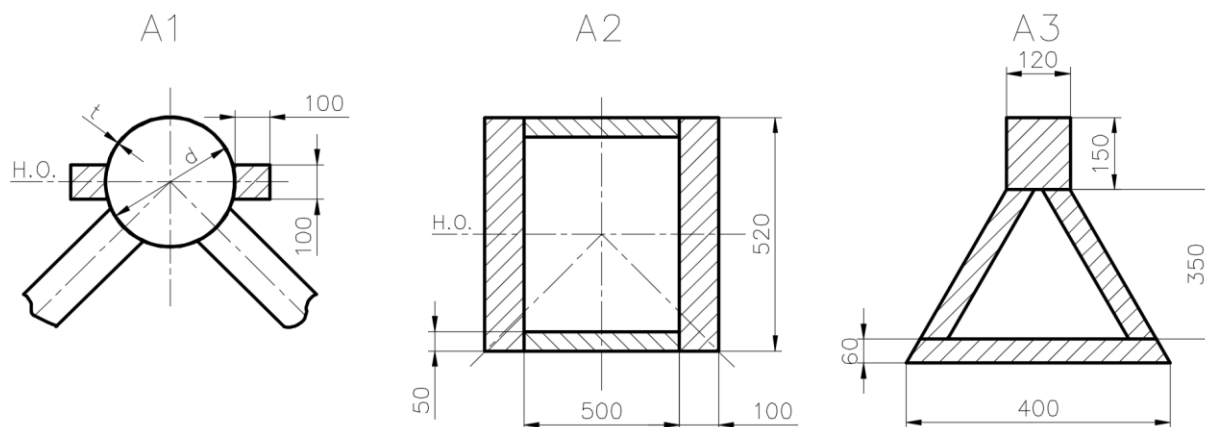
Схемы поперечного сечения реек: А1 – цилиндрические рейки; А2 – рейки прямоугольного сечения; А3 – рейки треугольного сечения
